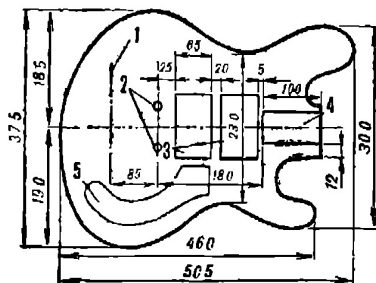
Корпус гитары: 1 — ось барабана струнодержателя; 2 — опорные полусферы; 3 — выемки для датчиков; 4 — место для грифа; 5 — выемка для платы.
